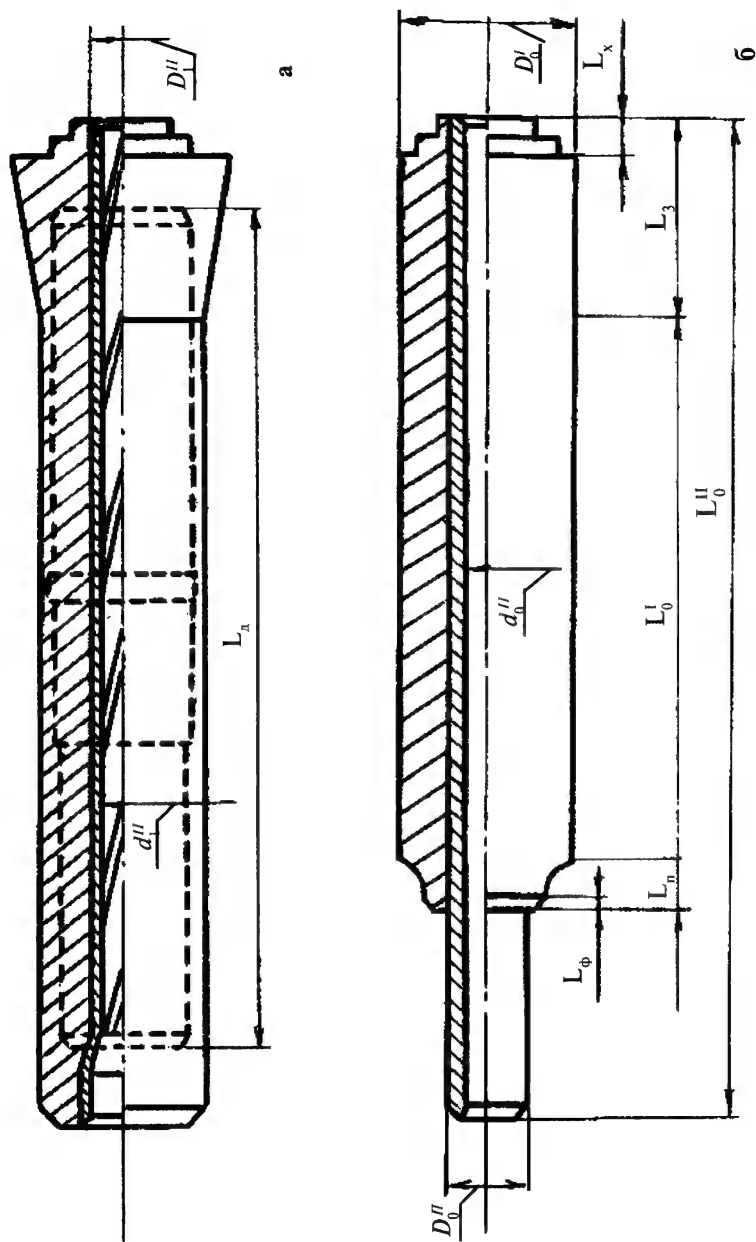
Схема к расчету размеров заготовок лейнированных стволот: а - поковка лейнированного (биметаллического) ствола, б - составная заготовка (сборный пакет)
